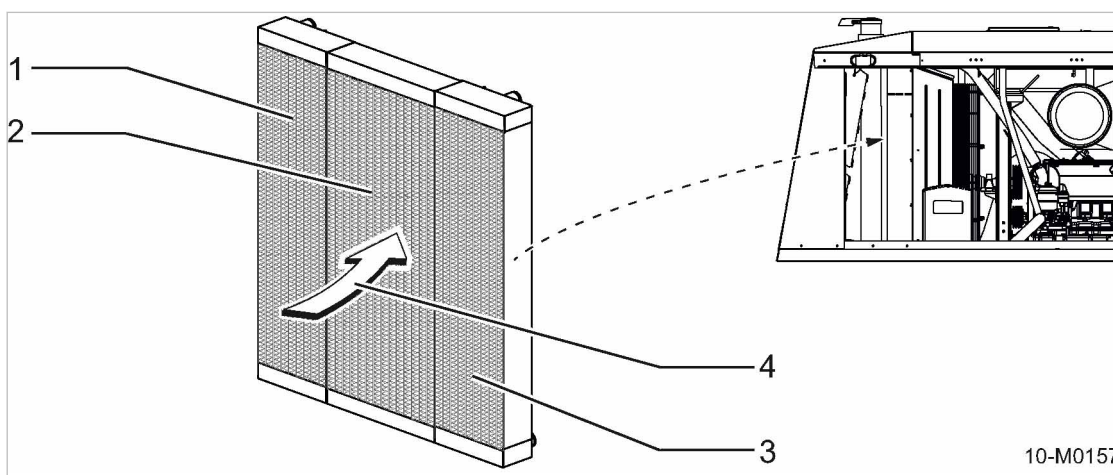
Limpieza de los refrigeradores del motor y del compresor
